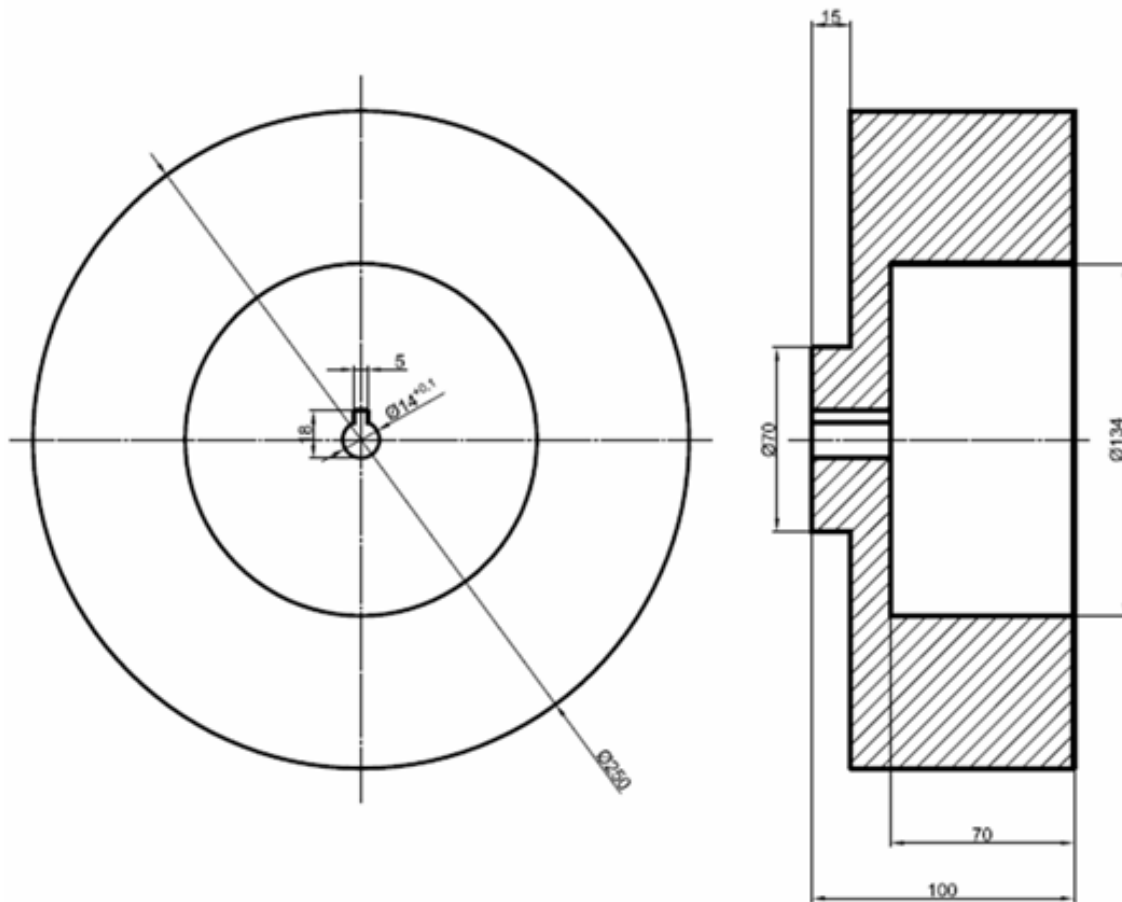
Чертеж заготовки рабочего колеса вентилятора
